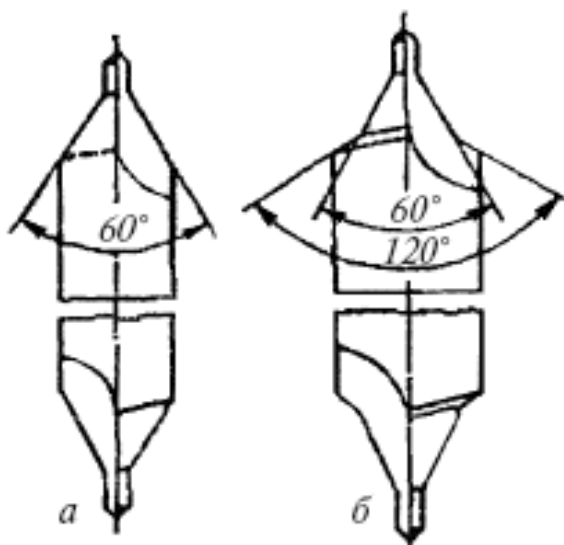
Центровочные сверла: а – обычные без предохранительного конуса; б – с предохранительным конусом
